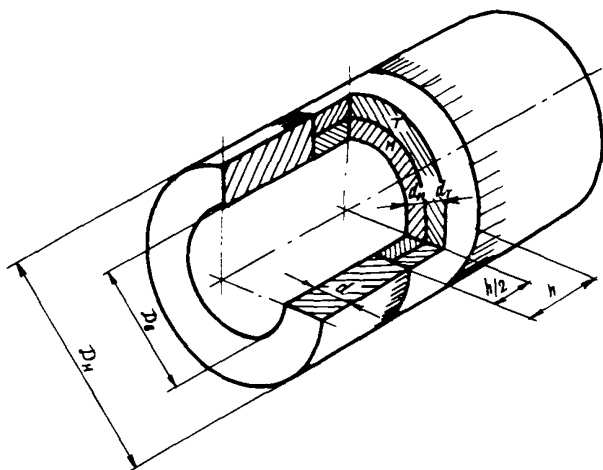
Схема сварного соединения трубы с кольцевой мягкой композитной прослойкой
